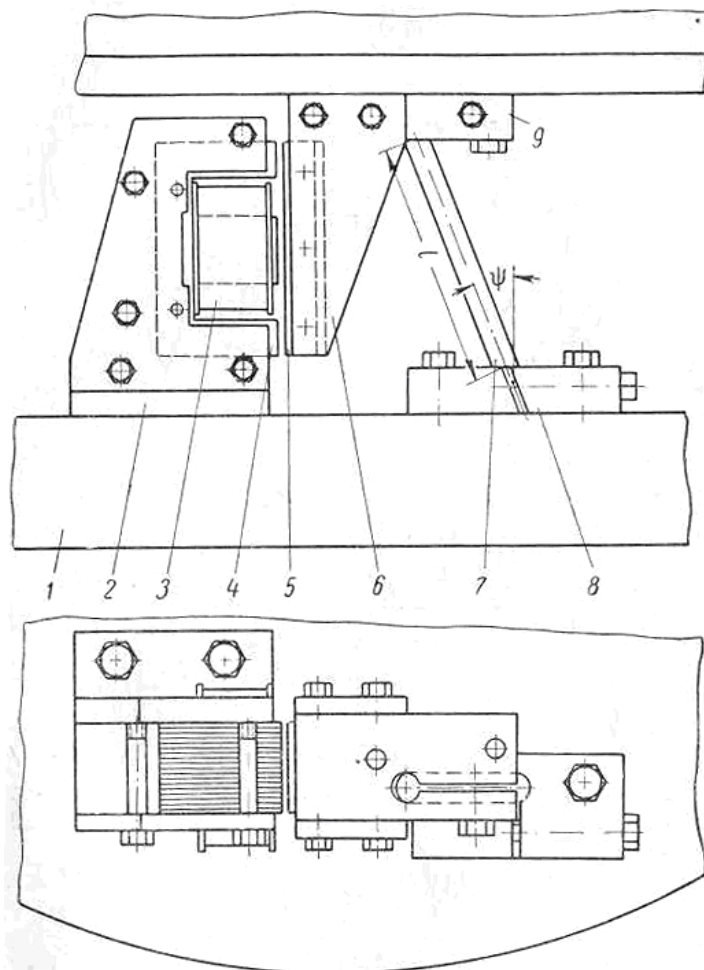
Конструкция вибратора и способ крепления пружинных стержней трехмагнитного питателя
